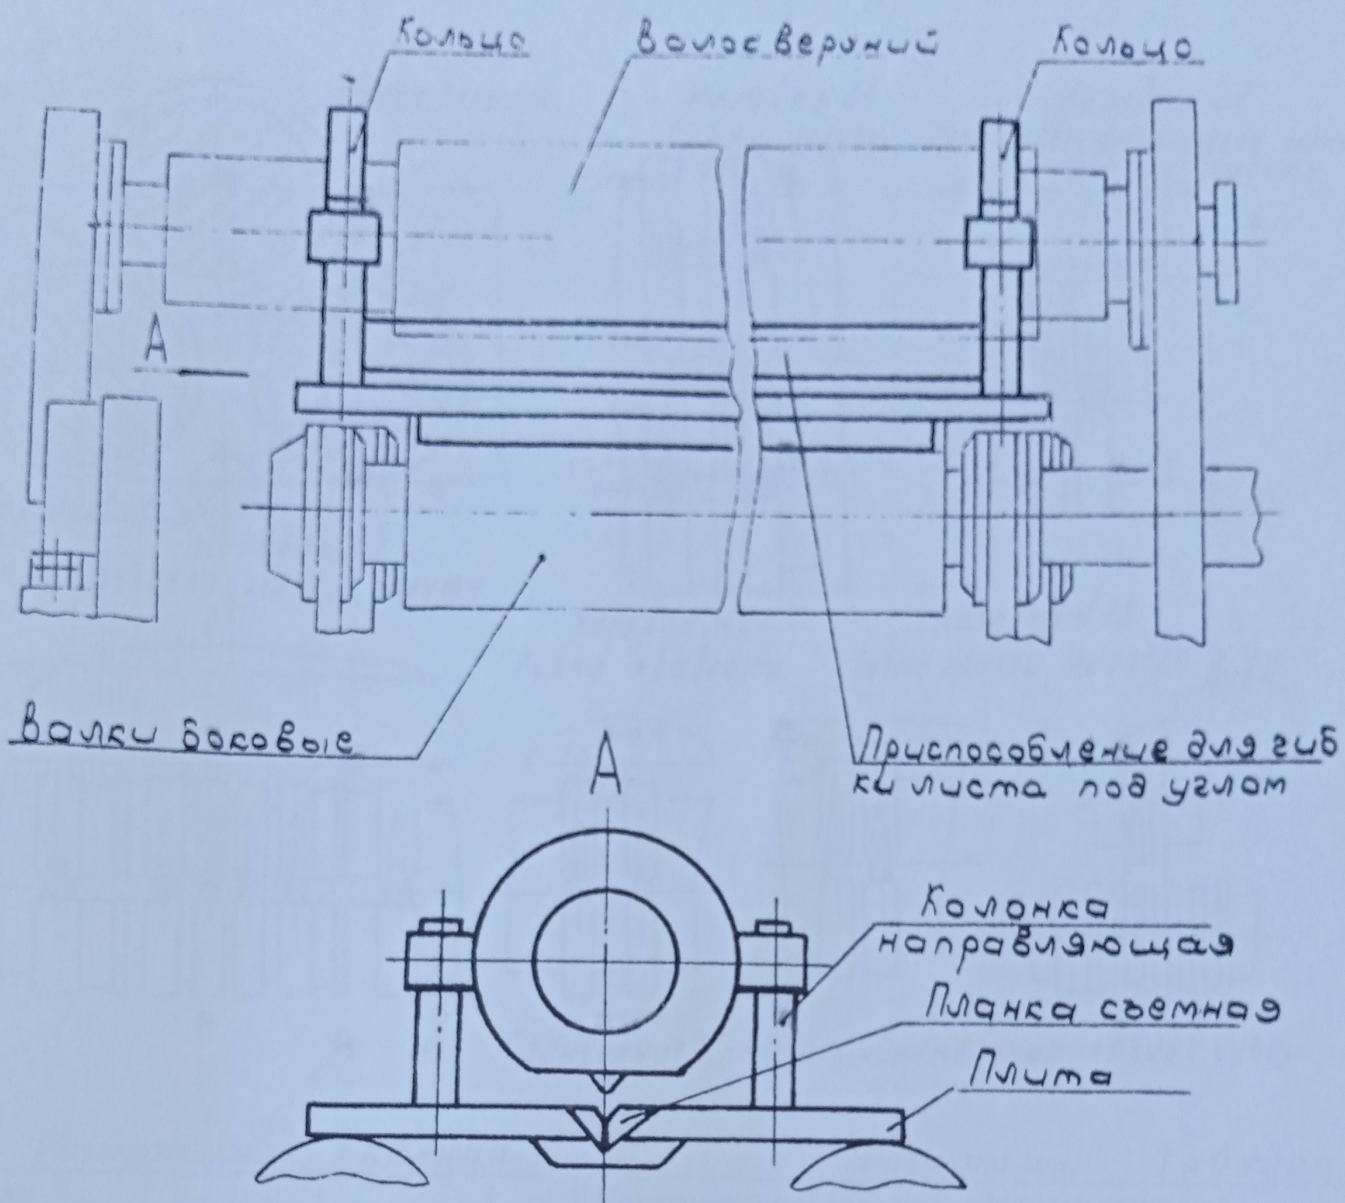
а. Установка приспособления для гибки листа под углом на машину ИБ2222
